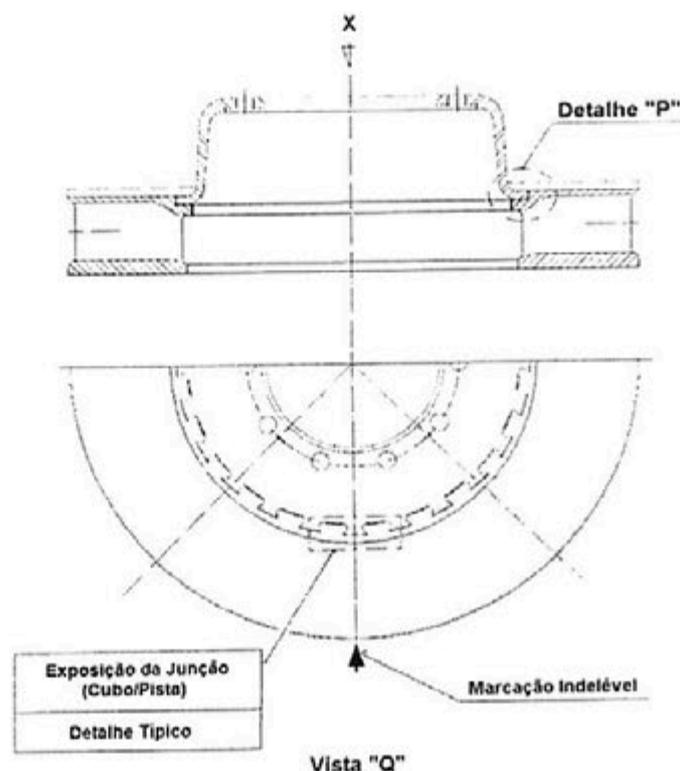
Exposição da solução de ancoragem (Cubo/Pista) – Usinagem
